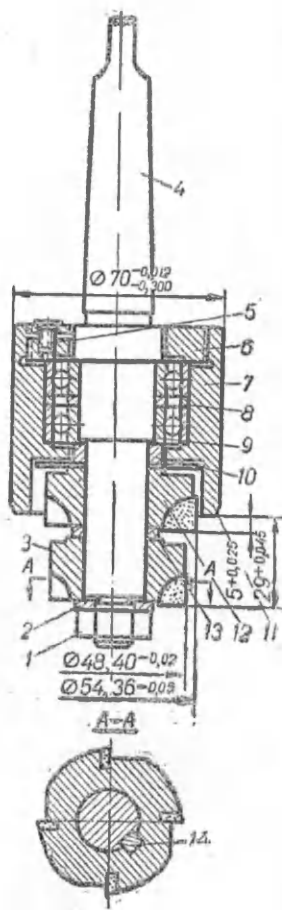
Оправка в сборе с зенкерами для обработки выточек под вставки камер сгорания головки цилиндра двигателя Д-40:
